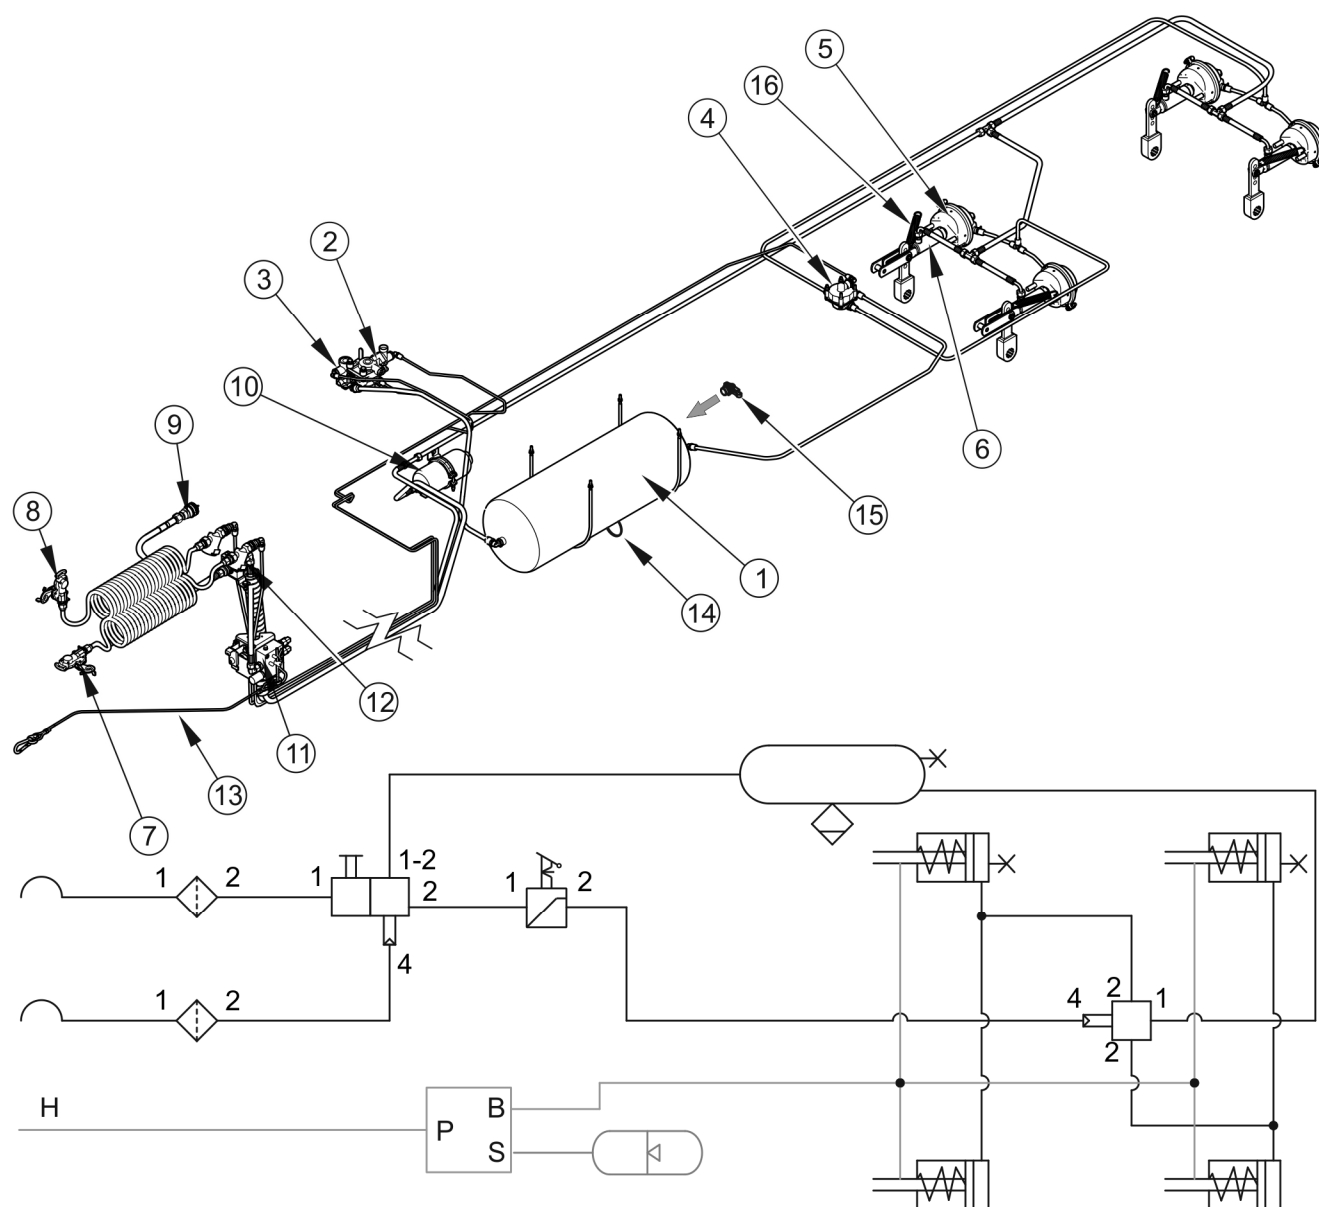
Konstrukce a schéma hydraulické brzdové instalace s mechanickým zajištěním
